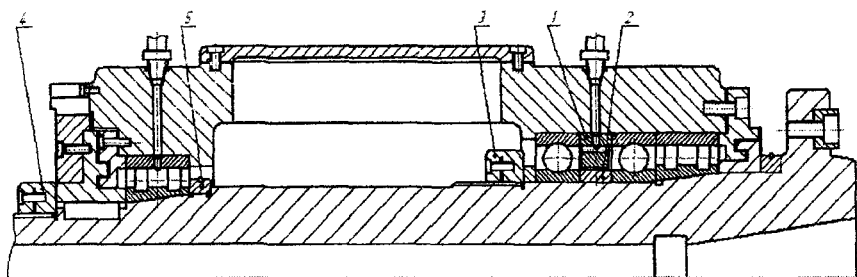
Шпиндельный узел с роликовыми радиальными двухрядными цилиндрическими подшипниками с коническим посадочным отверстием типа 3182100 в передней опоре в комплекте с шариковыми радиально-упорными подшипниками и в задней — самостоятельно
